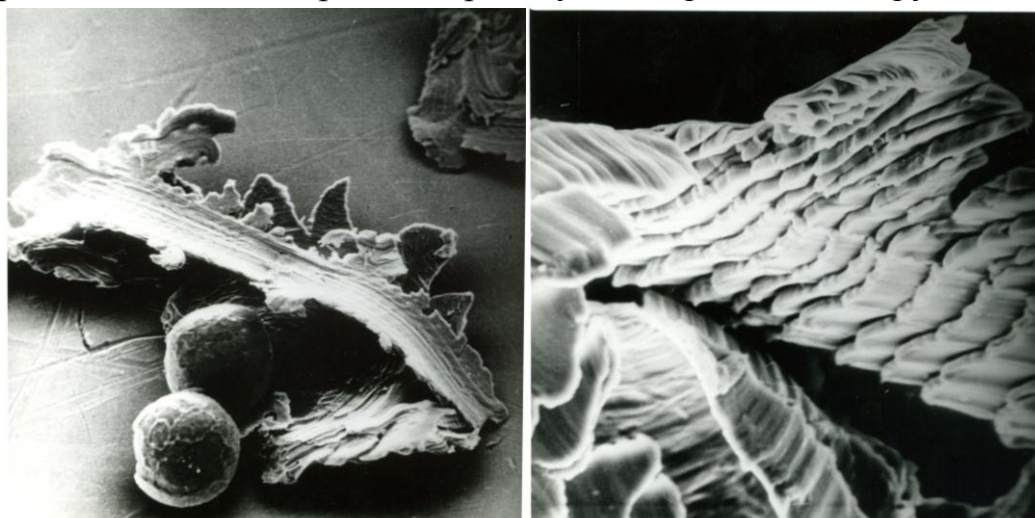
Фотоснимки микростружек, образующихся при шлифовании прерывистыми кругами с разным числом режущихся выступов
